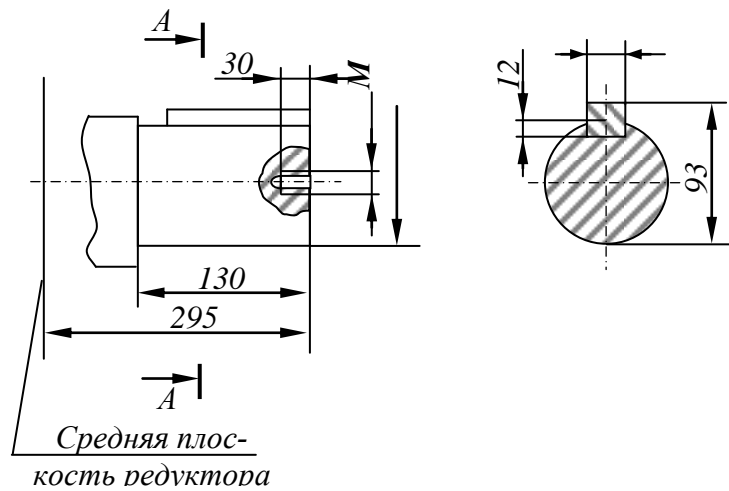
П7 Размеры цилиндрического конца выходного вала редуктора 1ЦЗУ-250
